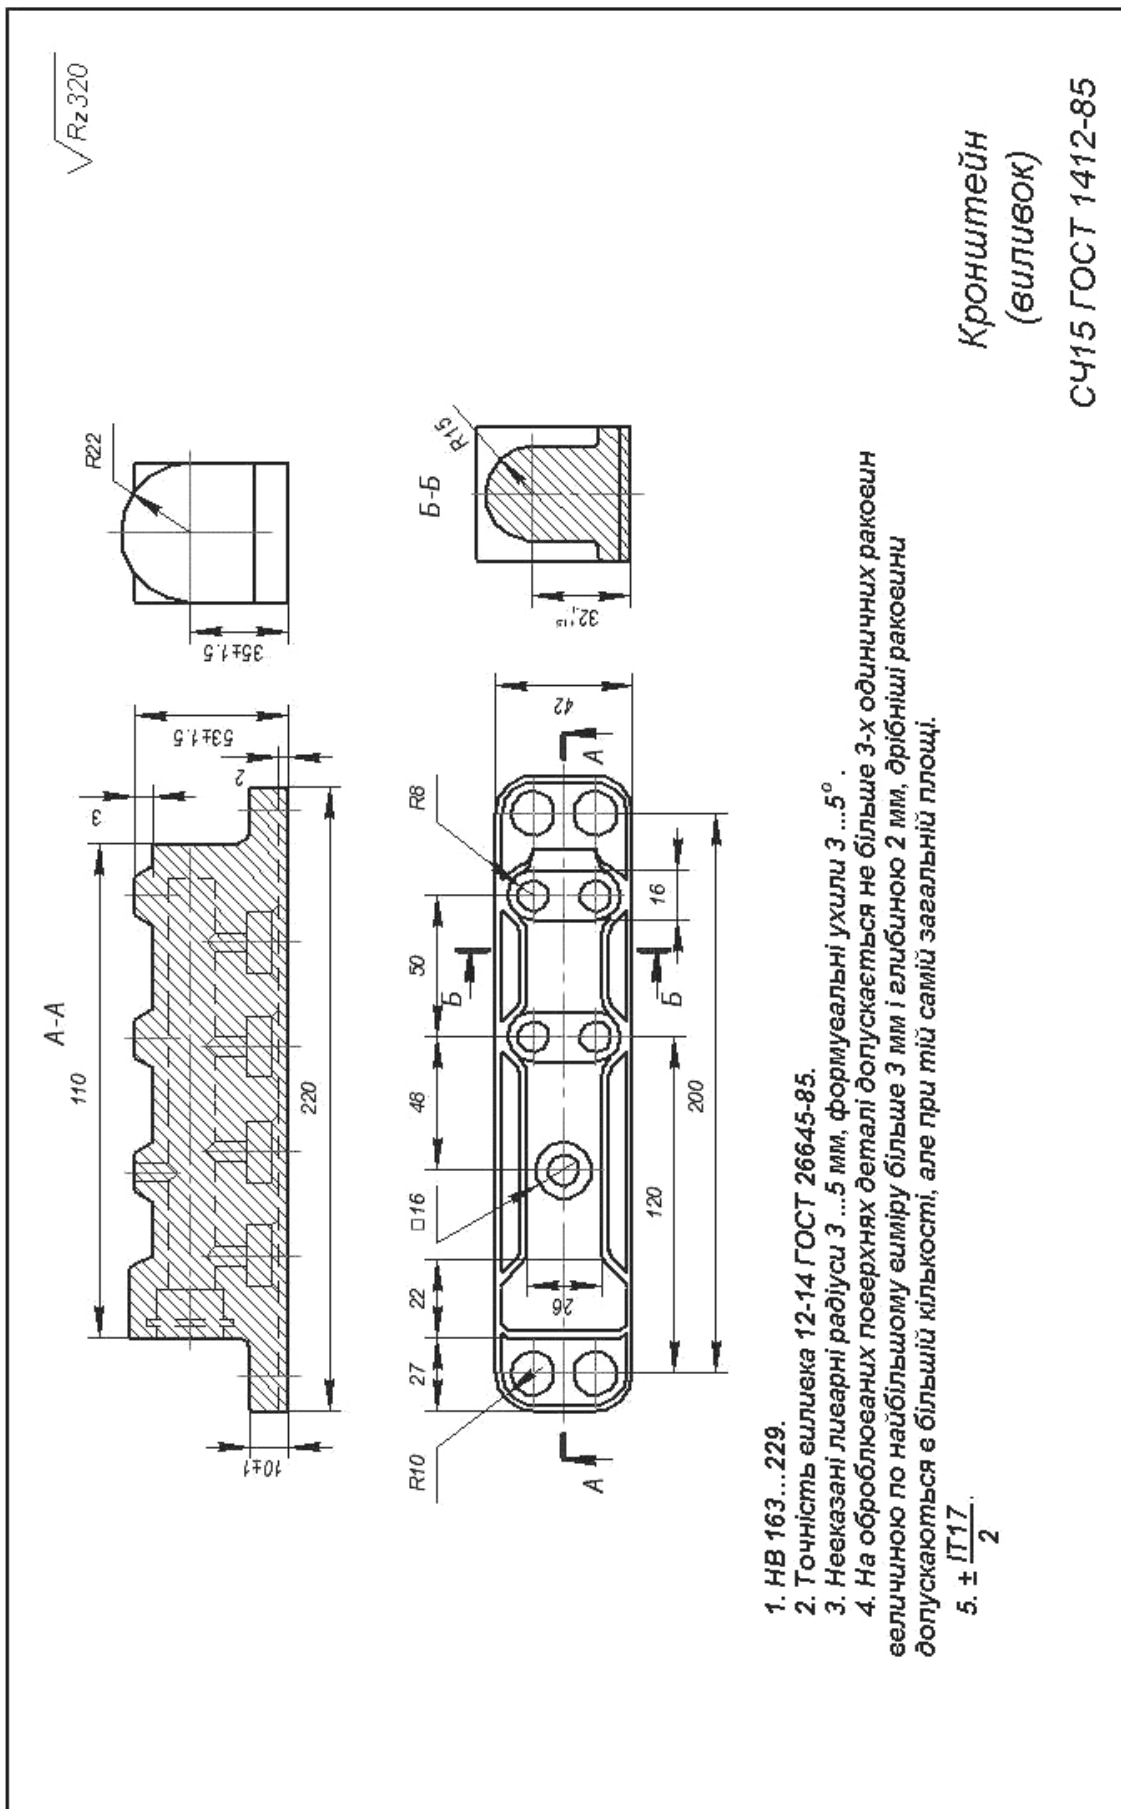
Заготовка корпусу, одержана методом литва
